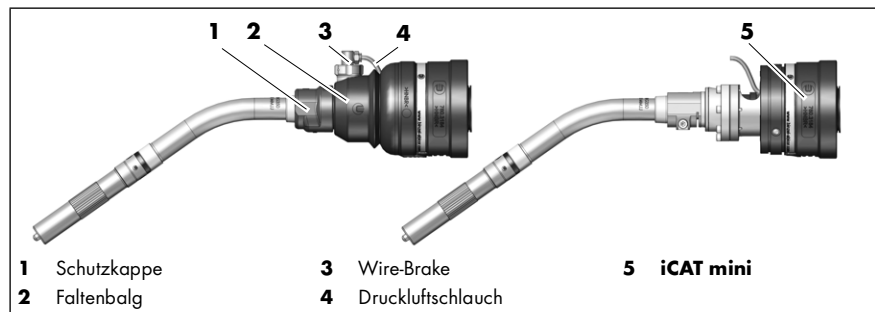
Reinigung – iCAT mini mit Wire-Brake und Schweißbrennerhals ABIROB® G
